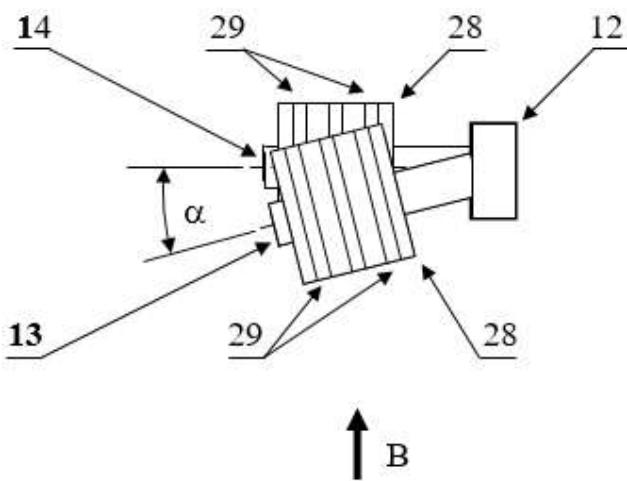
Элементы конструкции предложенного распиловочного устройства (фрагмент вида А): 12 – шарнир равных угловых скоростей, передающий крутящий момент от шкива клиноременной передачи 28 верхнему (ведомому) приводному валу 3; 13 – хвостовик под шкив 25 (см. рис. 2) клиноременной зубчатой передачи верхнего (ведомого) приводного вала 3; 14 – хвостовик под шкив 28 клиноременной зубчатой передачи нижнего (ведущего) приводного вала 4; 28 – шкив клиноременной зубчатой передачи; 29 – клиновые зубчатые ремни клиноременной зубчатой передачи; α – угол поворота в горизонтальной плоскости хвостовика верхнего (ведомого) приводного вала 3
